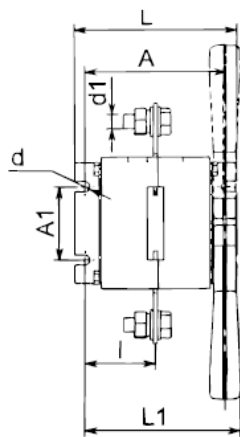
Выключатель-разъединитель однополюсный на одно направление с боковой рукояткой.
